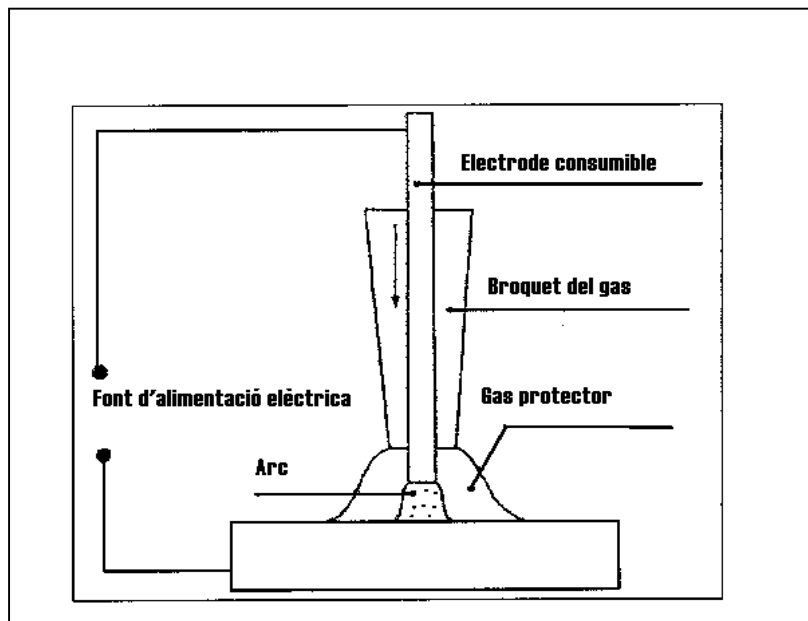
Esquema bàsic de soldadura elèctrica a l'arc amb protecció gasosa
